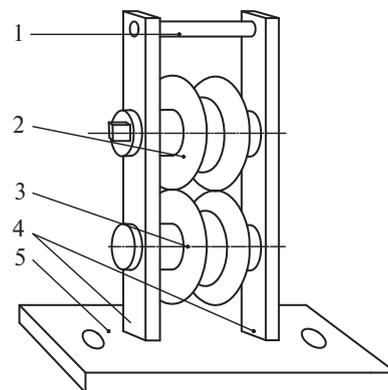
Общий вид установки с вращающимися матрицами для обжима втулок:
